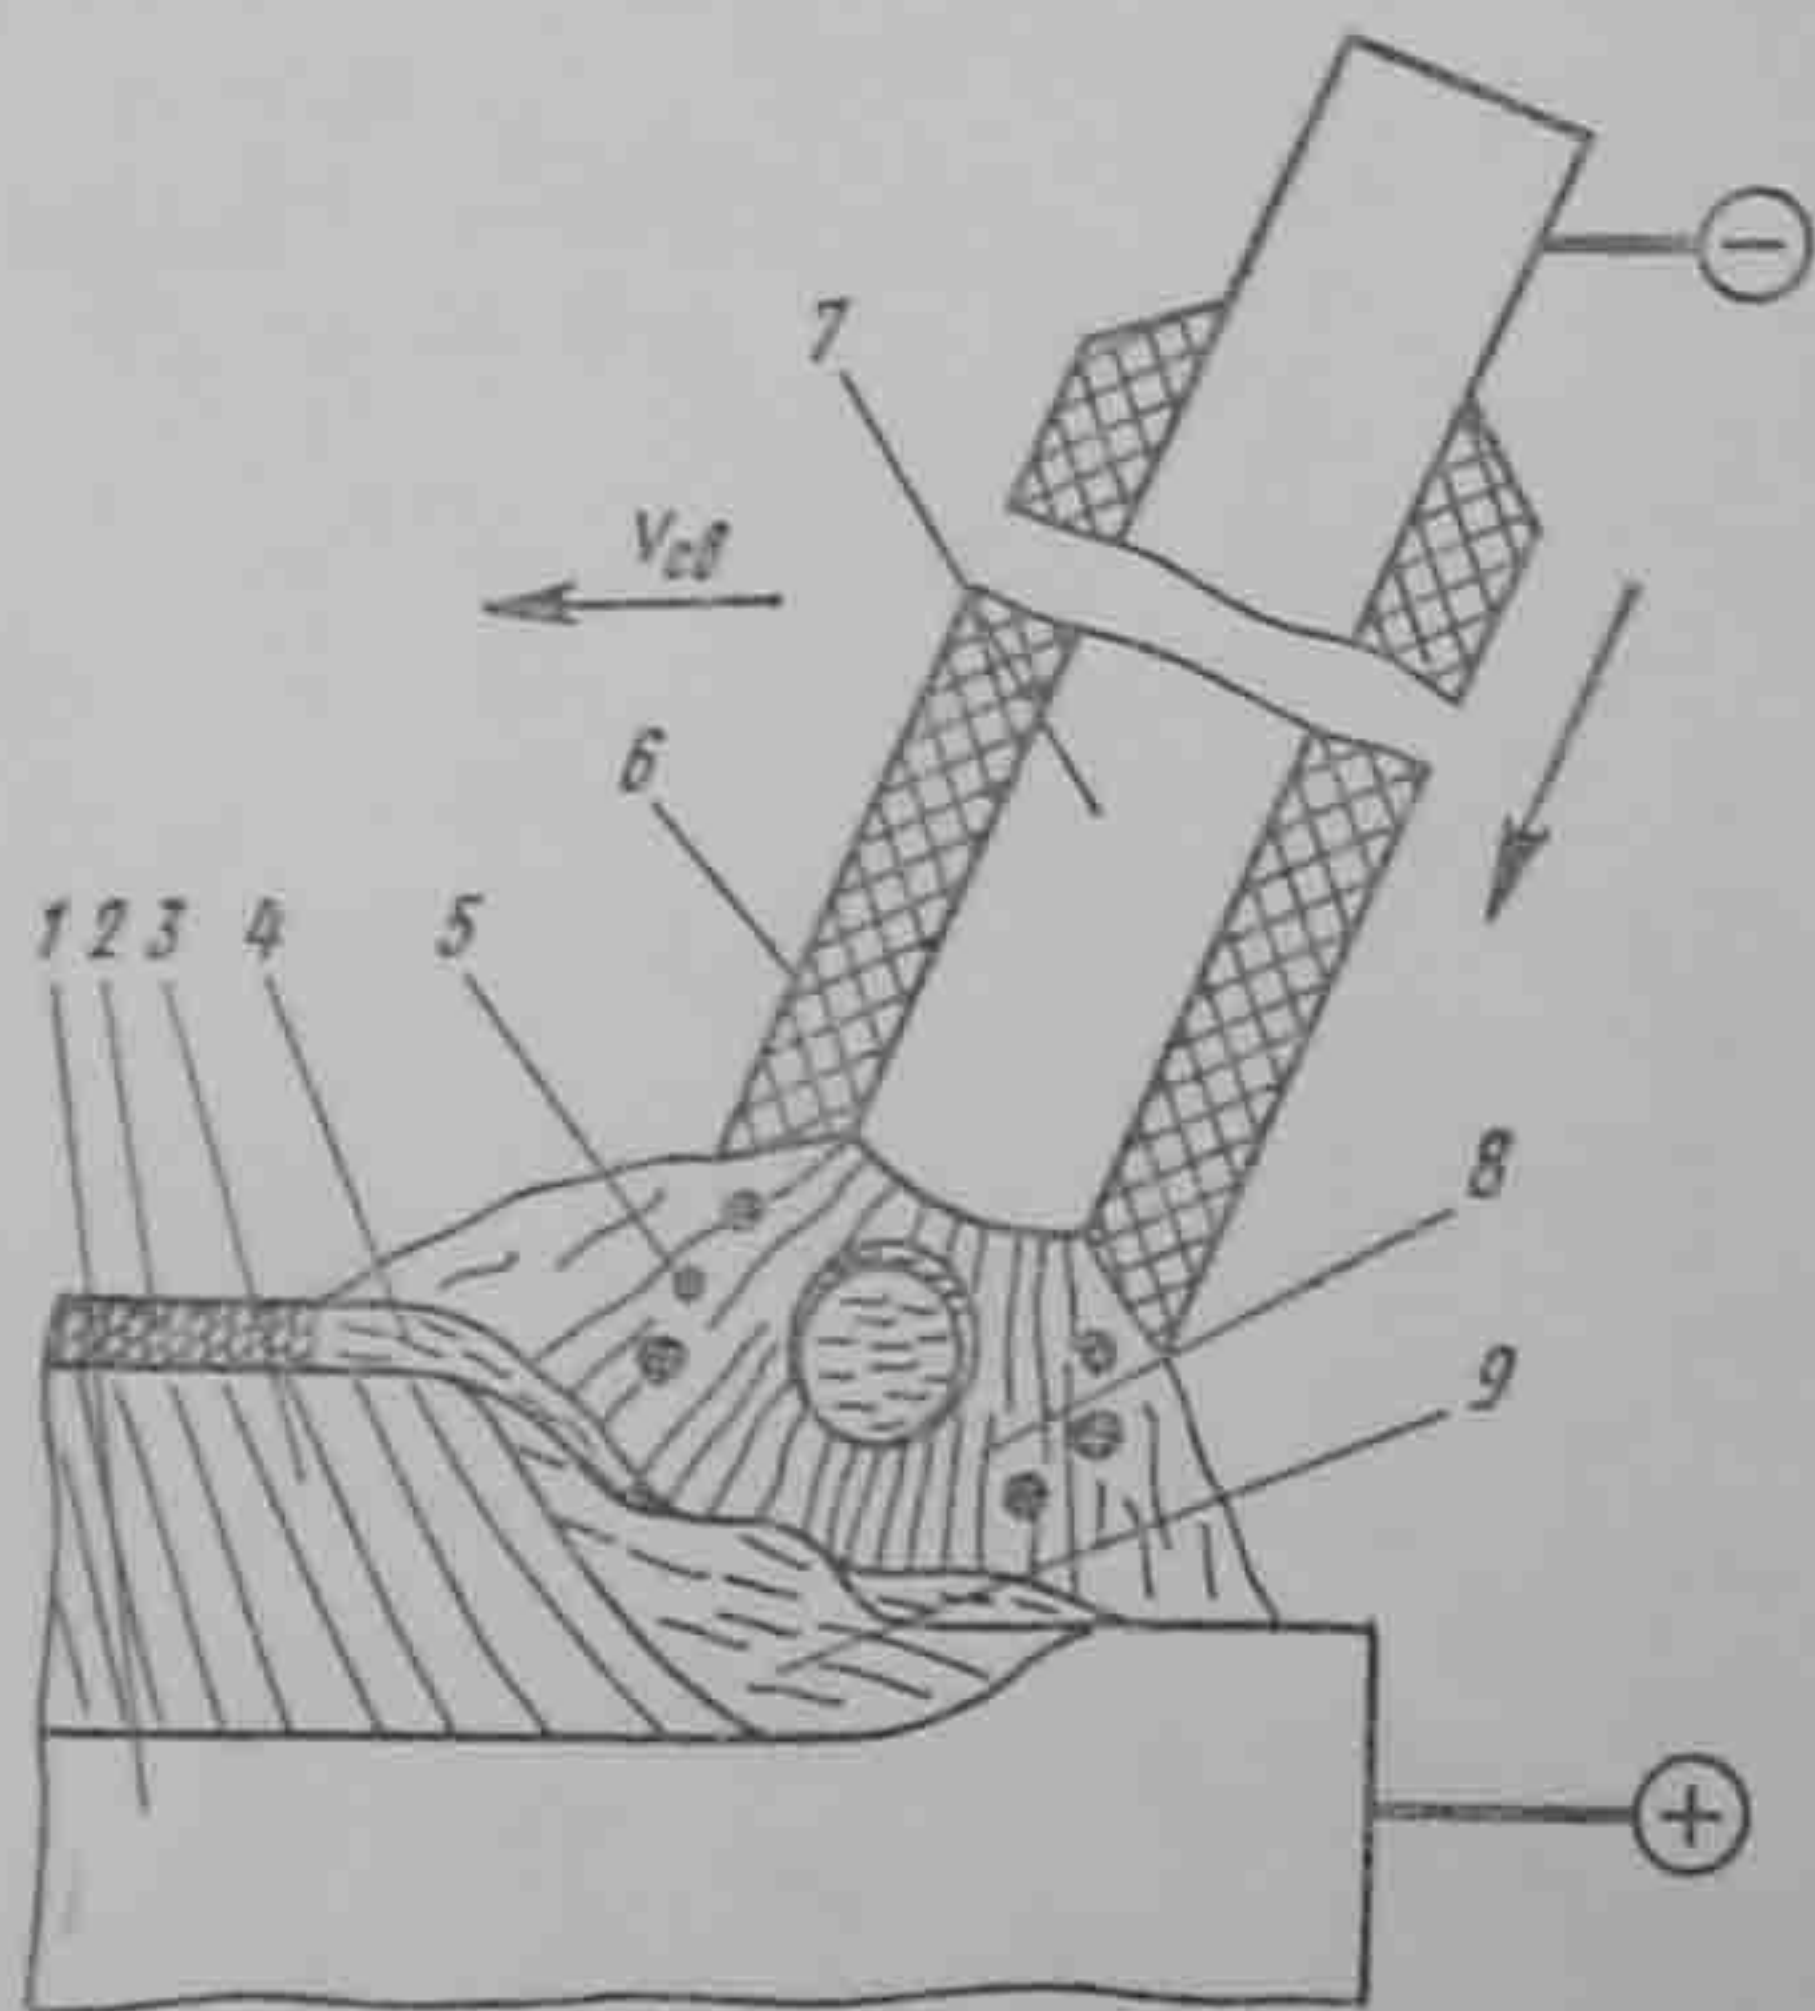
Схема сварки металлическим покрытым электродом
